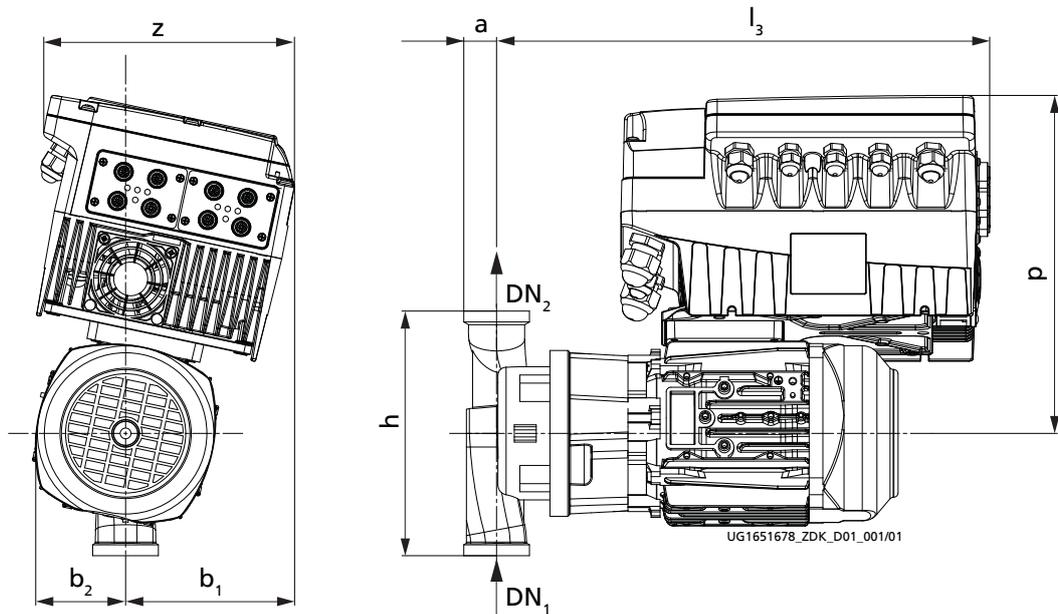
Abmessungen Pumpenaggregat mit PumpDrive 2 Eco, mit Gewindeanschluss, Baugröße < 032-032-100
